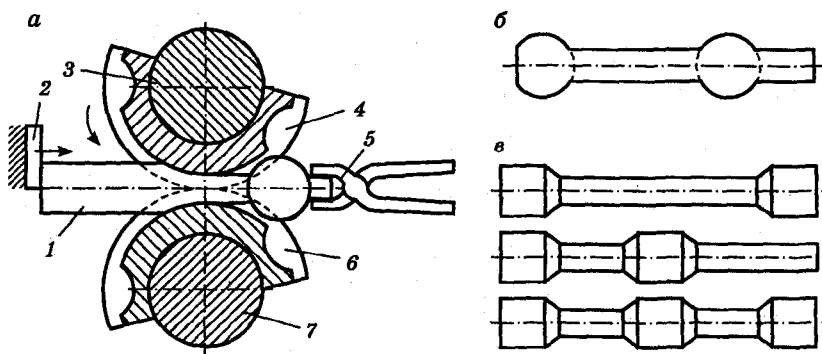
Схема вальцовки (а) и примеры получаемых заготовок (б) и поковок (в)
